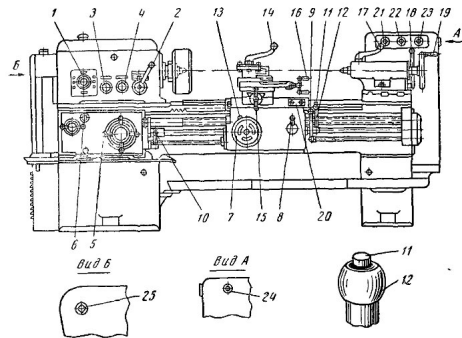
Общий вид токарно-винторезного станка модели 1К62 и схема органов управления
